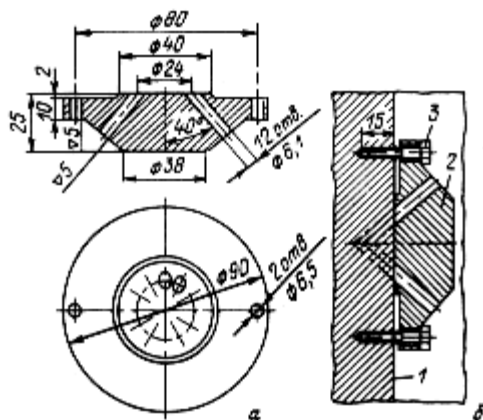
Кондуктор для вырезки образца из стенки аппарата: а - устройство; б - установка на стенке аппарата для высверливания образца; 1 - стенка аппарата; 2 - кондуктор; 3 - болт М6 × 25
